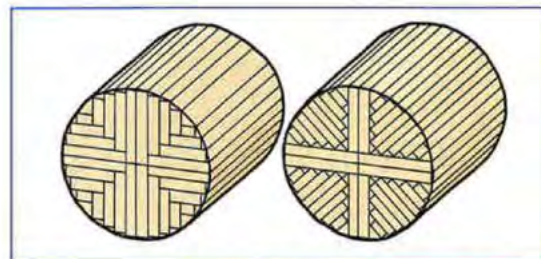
Je kunt op verschillende manieren planken of balken uit een boom zagen.
